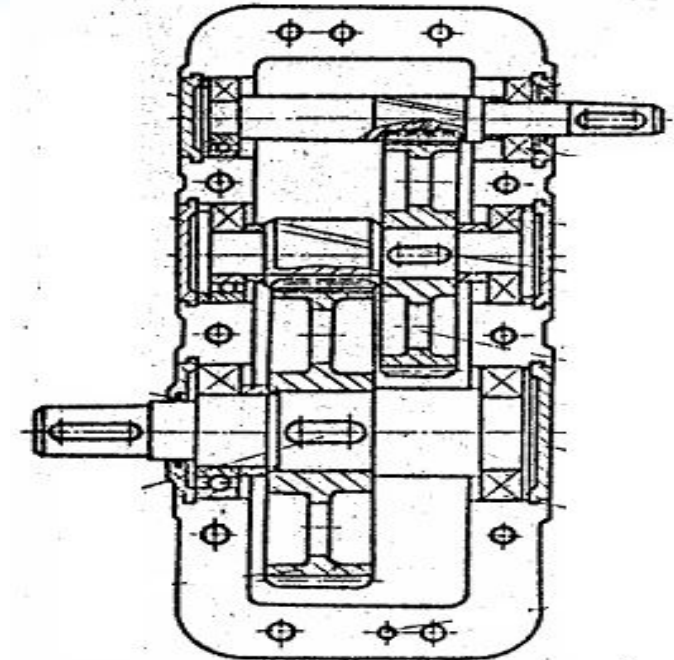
б - Двухступенчатый цилиндрический редуктор вертикальный
